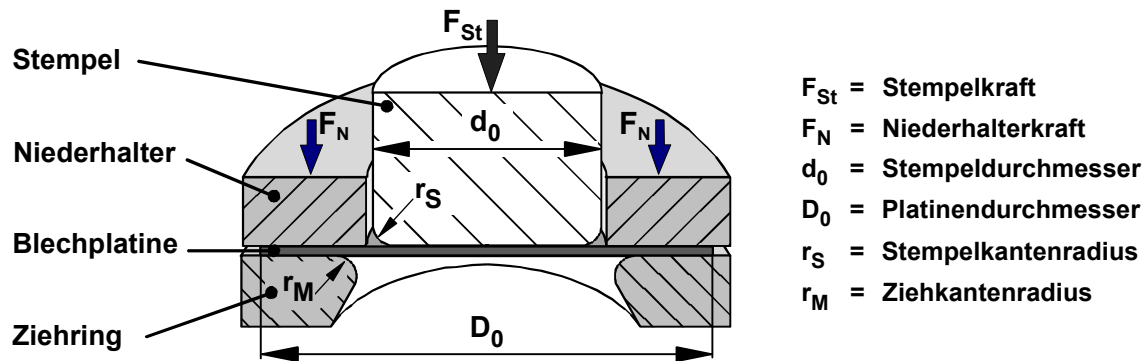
Prinzipieller Werkzeugaufbau und Bezeichnungen beim Tiefziehen
